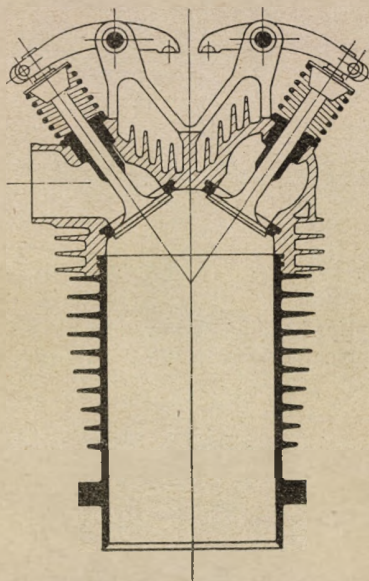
Válec a ventilová hlava motoru *N. F.
